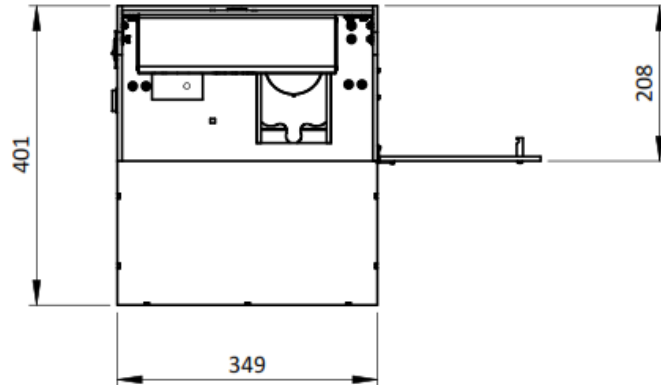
Esquema superior estructural dimensional de la impresora.
